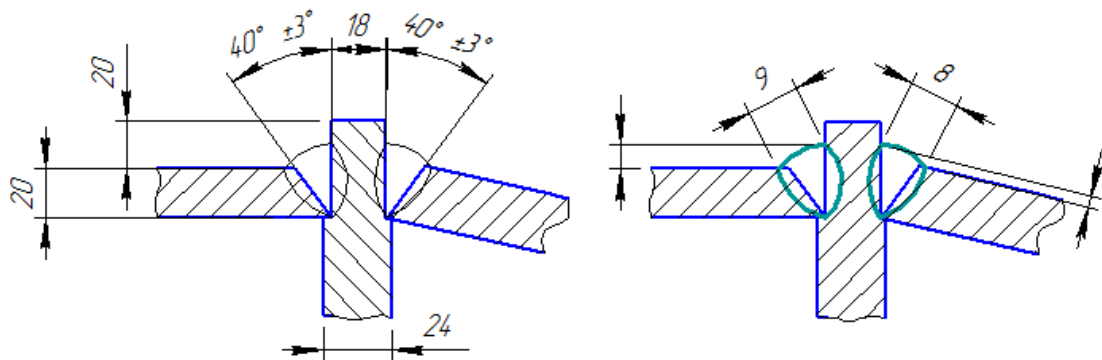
Форма и размеры сварного соединения III
